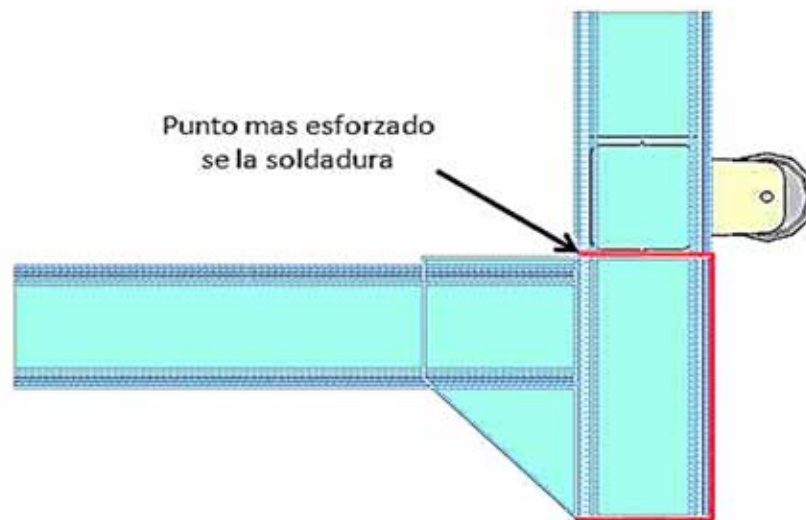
Localización del punto más esforzado en la soldadura.
